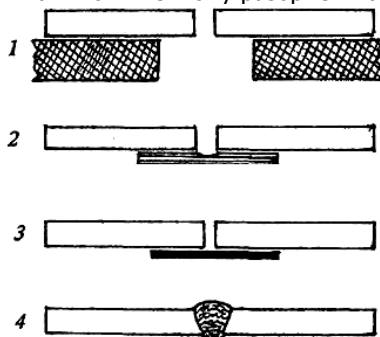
Сварка стыковочных швов. 1 — сварка шва «на весу»; 2 — сварка на медной подкладке (съёмной); 3—сварка на стальной остающейся подкладке; 4— сварка с предварительным и подварочным швом
